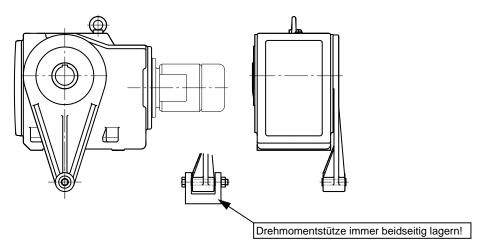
Befestigung der Drehmomentstütze bei Kegelrad- und Schneckengetrieben
